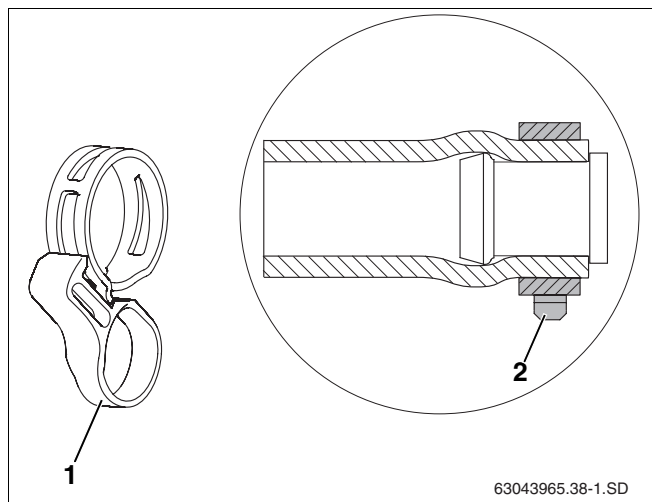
Braçadeira de mola com anel de fixação e no estado montado no bujão cego pré-montado.
